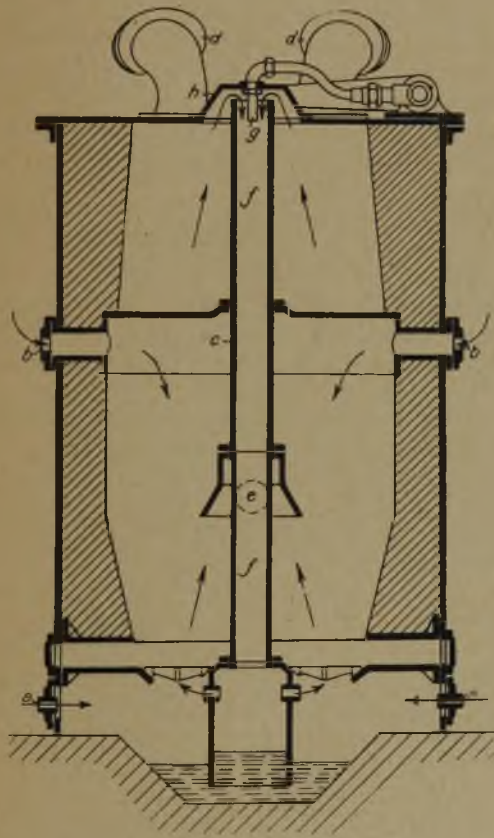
Gaserzeuger der Gasmotorenfabrik Deutz.
